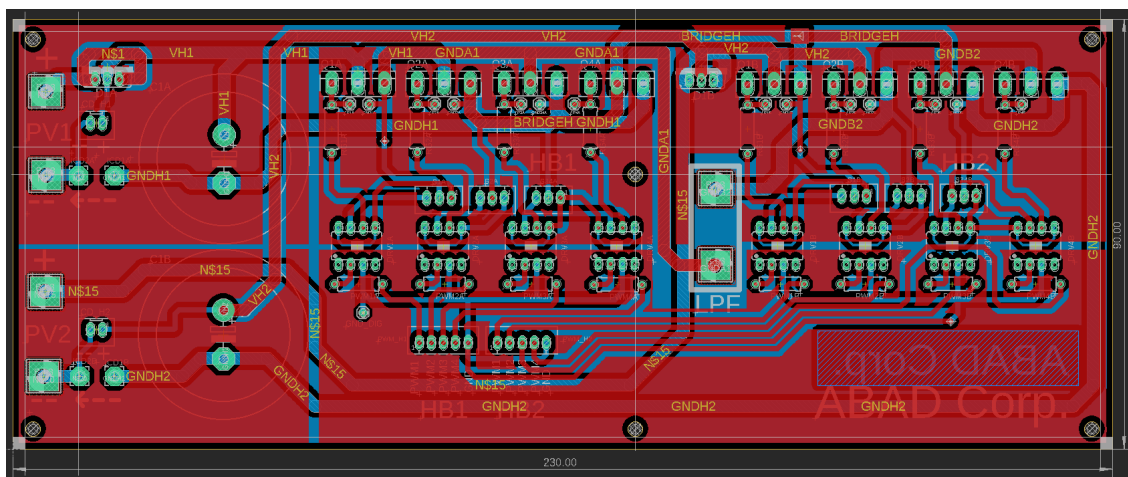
Vista de PCB obtenido de EAGLE CAD.
